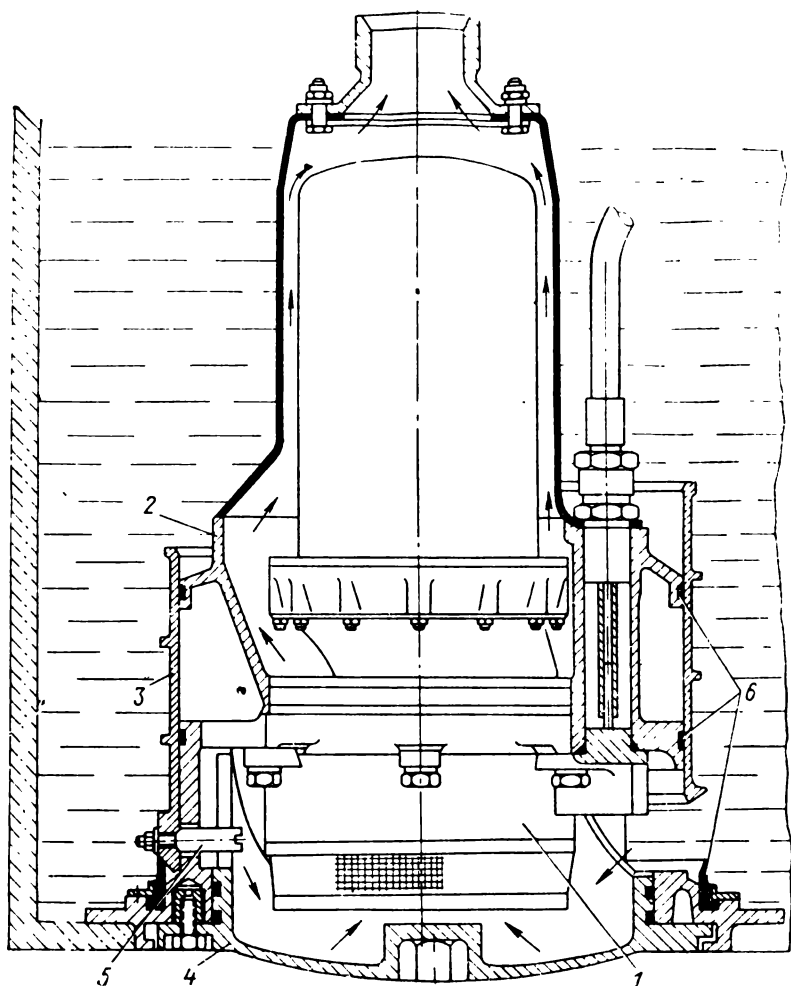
Кессонное монтажное устройство для монтажа и демонтажа насосного агрегата без слива топлива из кессона, устанавливаемое на самолете «Комета»:
